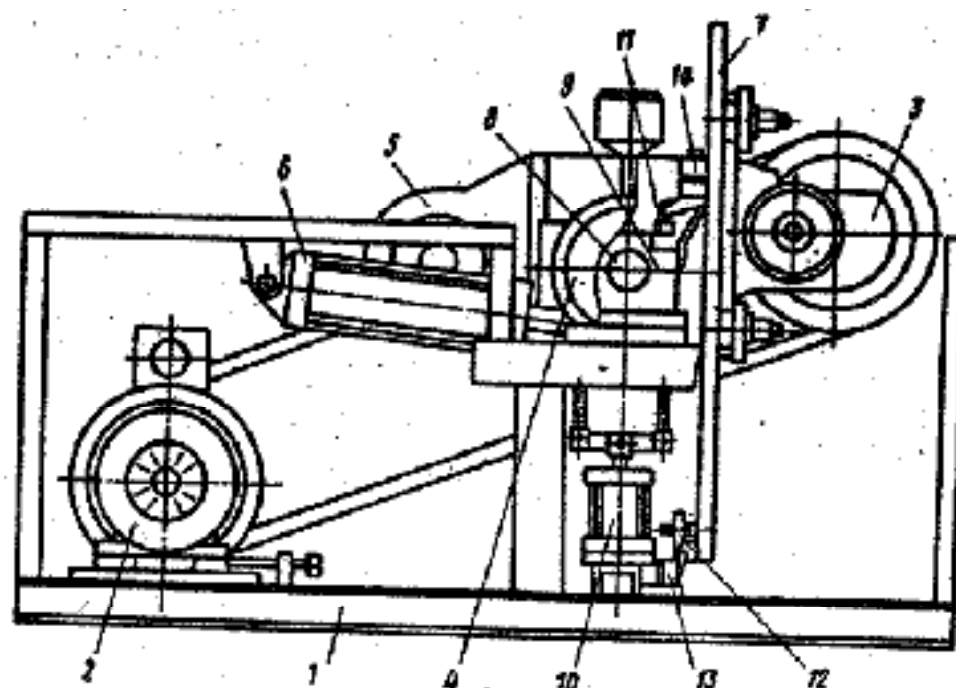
Стенд для испытания и обкатки коробок передач
